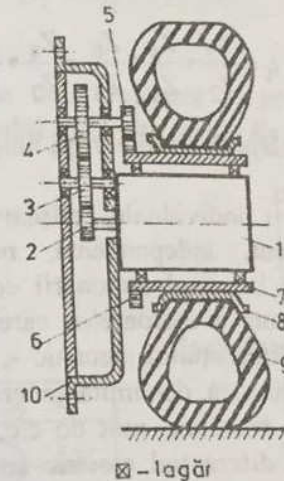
Schema unei motoroți cu acționare prin angrenaj.
